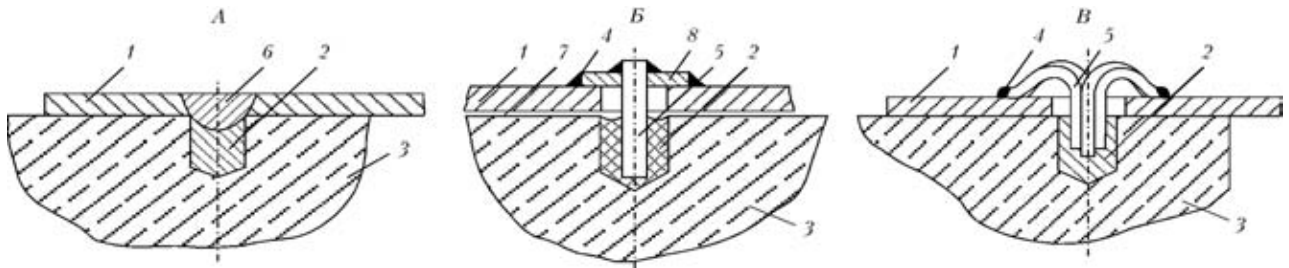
Схемы сварных соединений «металл – углеродный материал» разных вариантов (А–В): 1 — металлическая пластина; 2 — ЭКП; 3 — углеродный блок; 4 — сварной шов; 5 — компенсатор; 6 — электрозаклепка; 7 — зазор между пластиной и углеродным блоком; 8 — шайба
